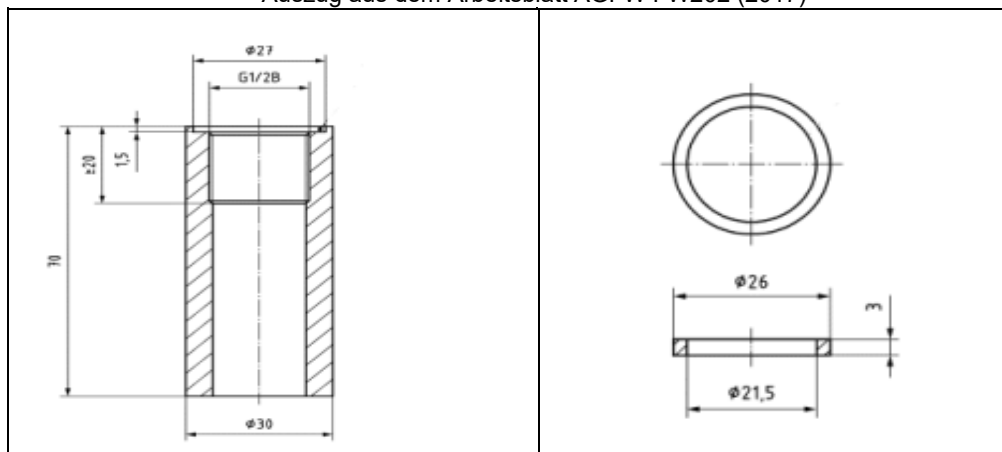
Einschweißmuffe mit Aussparung für Kupferdichtring > Qp6
